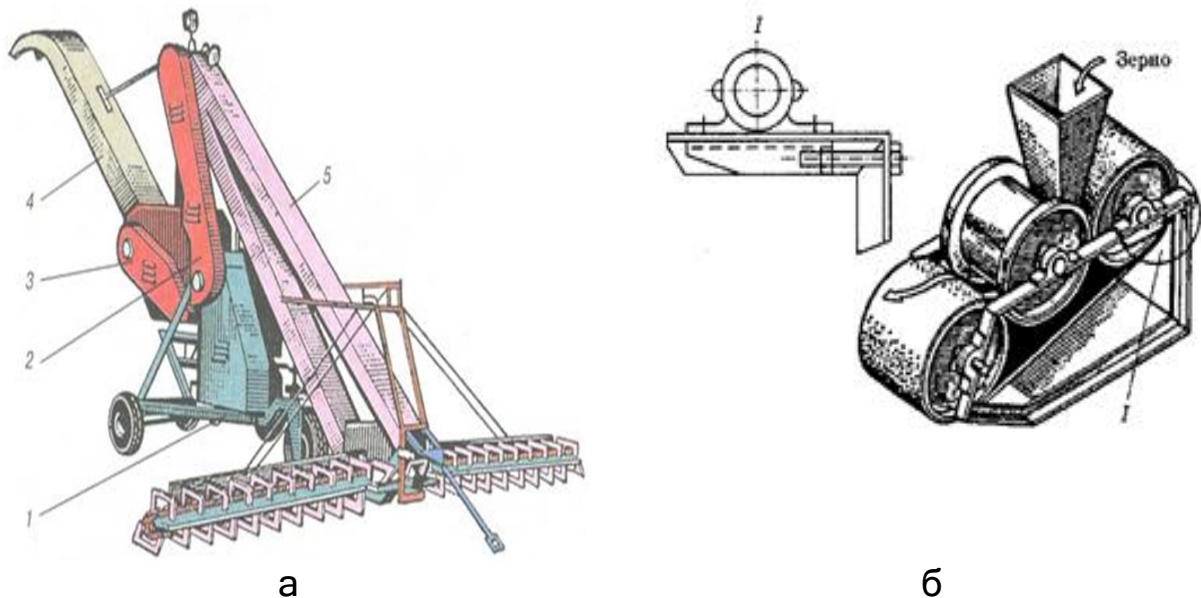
Зернометальник самопересувний ЗМ-60: а - загальний вигляд: 1 - рама з ходовою частиною; 2- контрпривід; 3- тример; 4 - напрямний кожух з козирком; 5 - завантажувальний конвеєр; б - загальний вигляд тримера: I - натяг стрічки.
